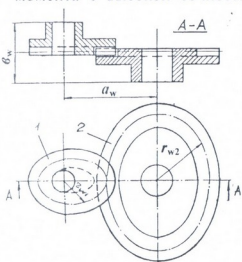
Торцовая зубчатая передача с некруглыми колесами
